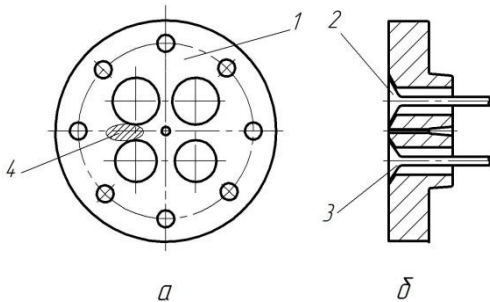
Схема огневого днища крышки цилиндра: *а* – вид со стороны рабочих газов; *б* – разрез по клапанам; 1 – крышка цилиндра; 2 – впускной клапан; 3 – выпускной клапан; 4 – трещины
